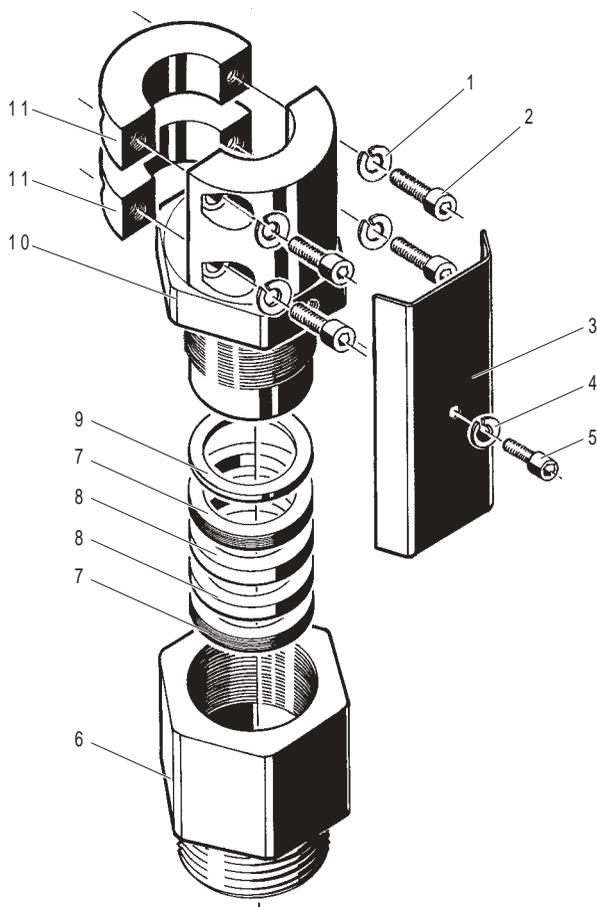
União rosca de fixação ARV-VB63.B - até 25 bar (362 psi)
